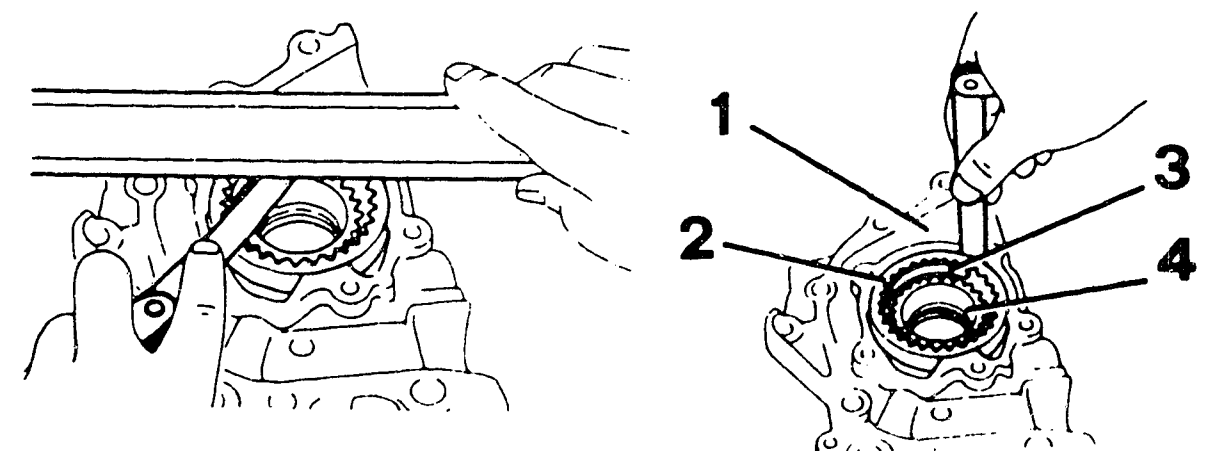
Motoren 4A-C und 4A-GE: Das Messen der Ölpumpenspiele: 1 Gehäuse – 2 Aussenzahnrad – 3 Sichel – 4 Antriebsrad.
